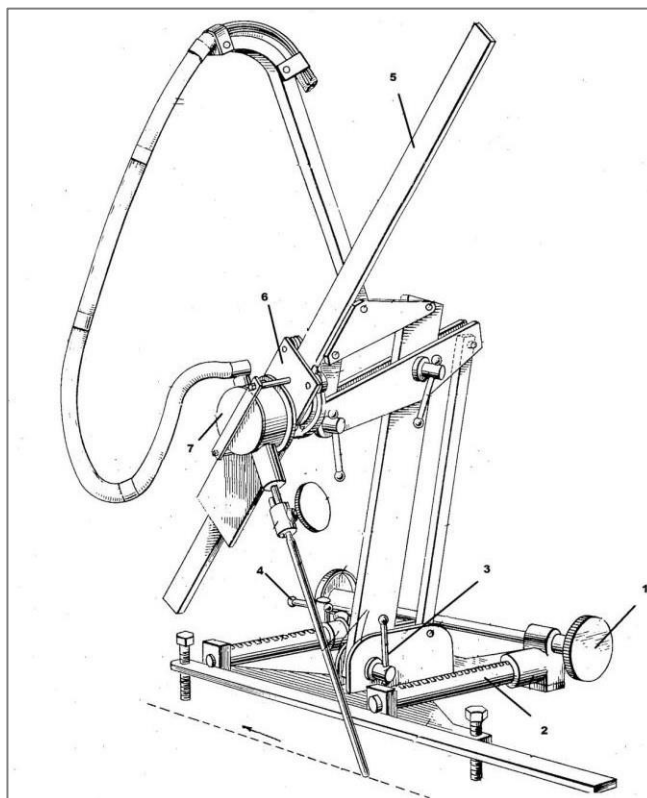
Внешний вид конструкции установки для гравитационной сварки прямолинейных швов
